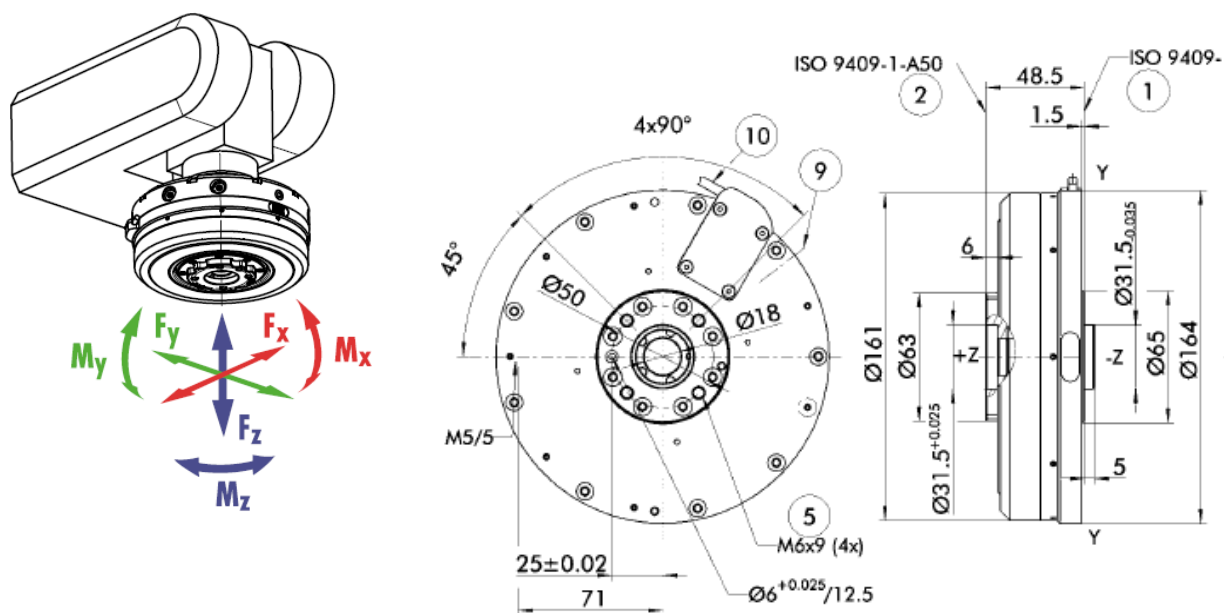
Виды силовых компонентов, измеряемых датчиками FTC-050, и габаритный чертеж
